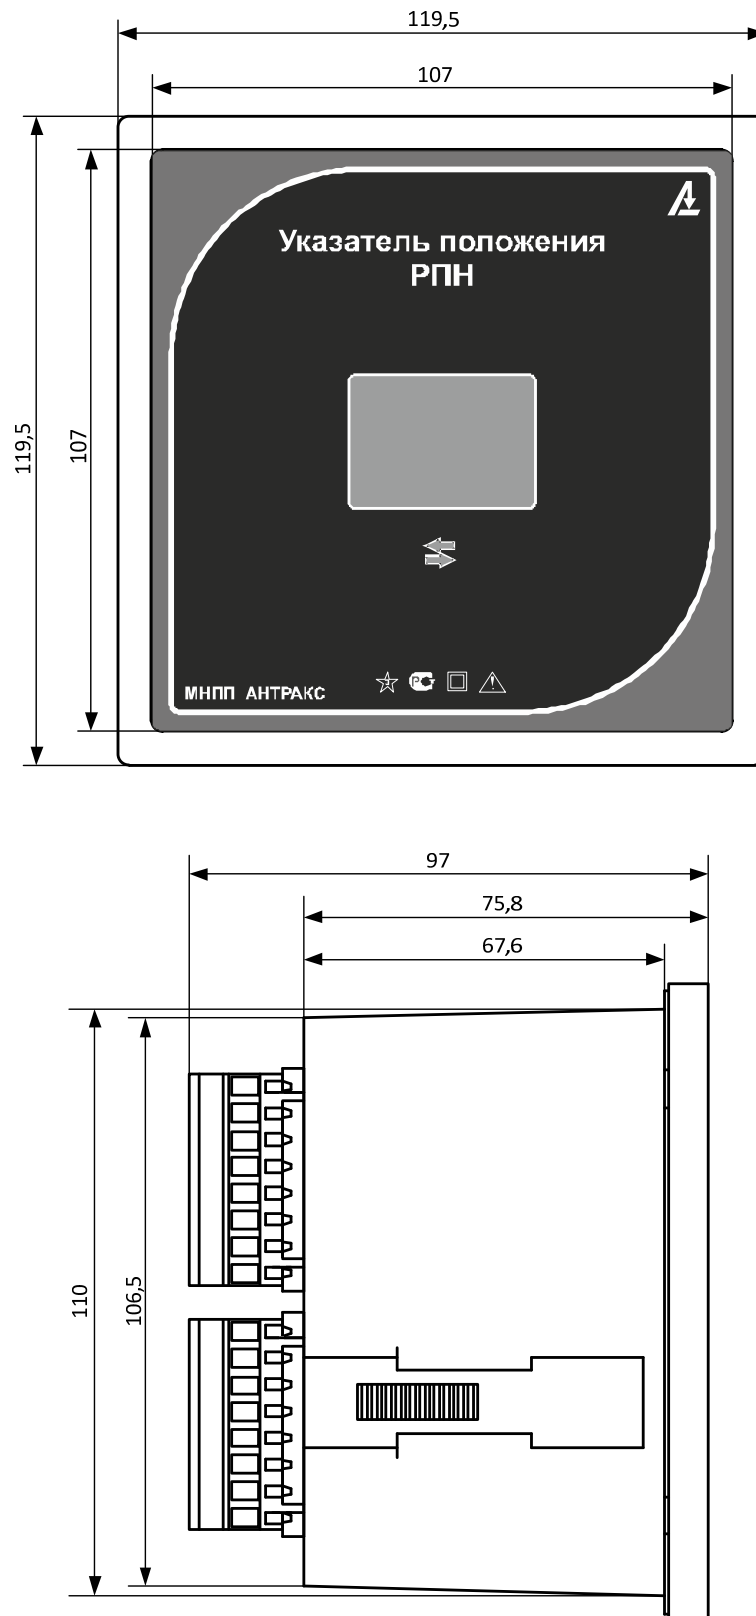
Габаритные размеры щитового варианта указателя положения РПН
